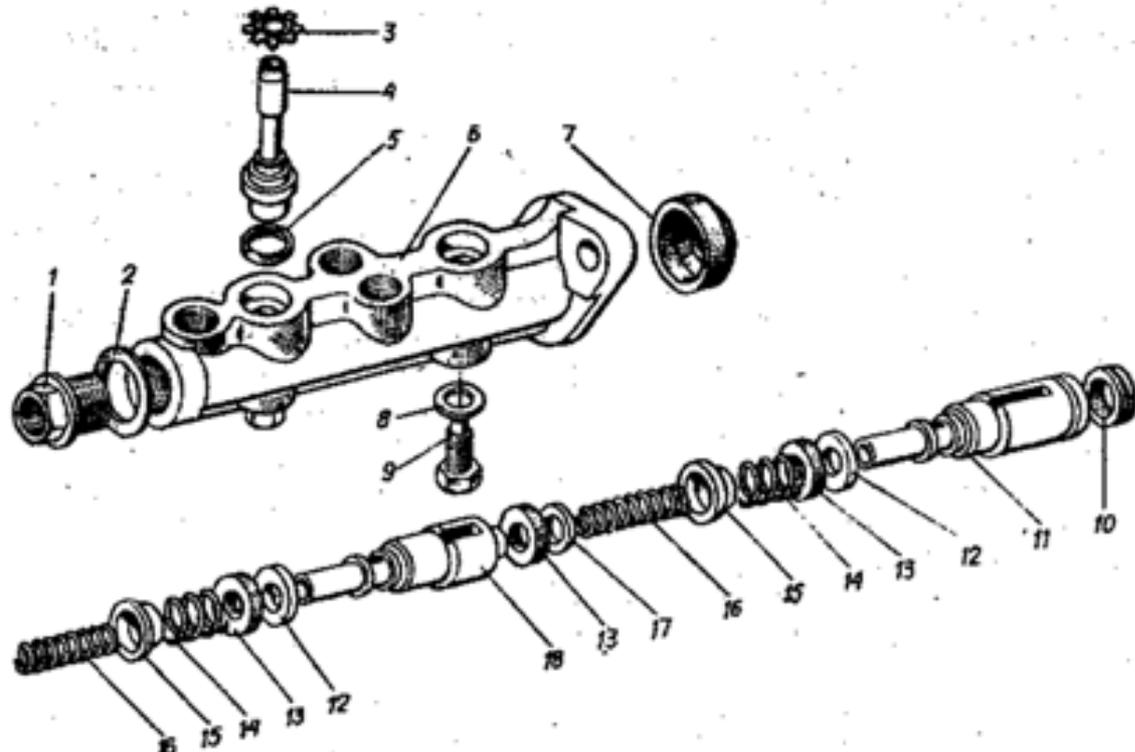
Детали главного цилиндра тормоза: 1 - пробка; 2 - прокладка; 3 - шайба стопорная; 4 - штуцер; 5 - прокладка штуцера; 6 - картер главного цилиндра; 7 - колпак защитный; 8 - прокладка; 9 - болт установочный; 10 - манжета уплотнительная; 11 - поршень правого переднего и заднего левого колес; 12 - втулка распорная; 13 - манжета высокого давления; 14 - пружина чашки; 15 - чашка; 16 - пружина поршня; 17 - шайба упорная; 18 - поршень левого переднего и заднего правого колес.
